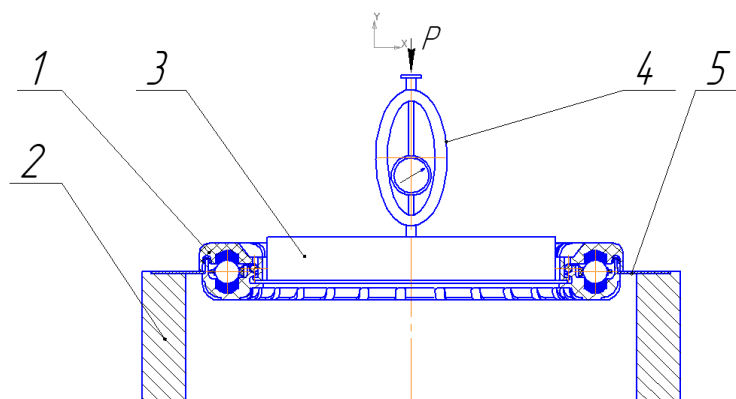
Схема установки для испытания фиксации замков кожухов подшипника
